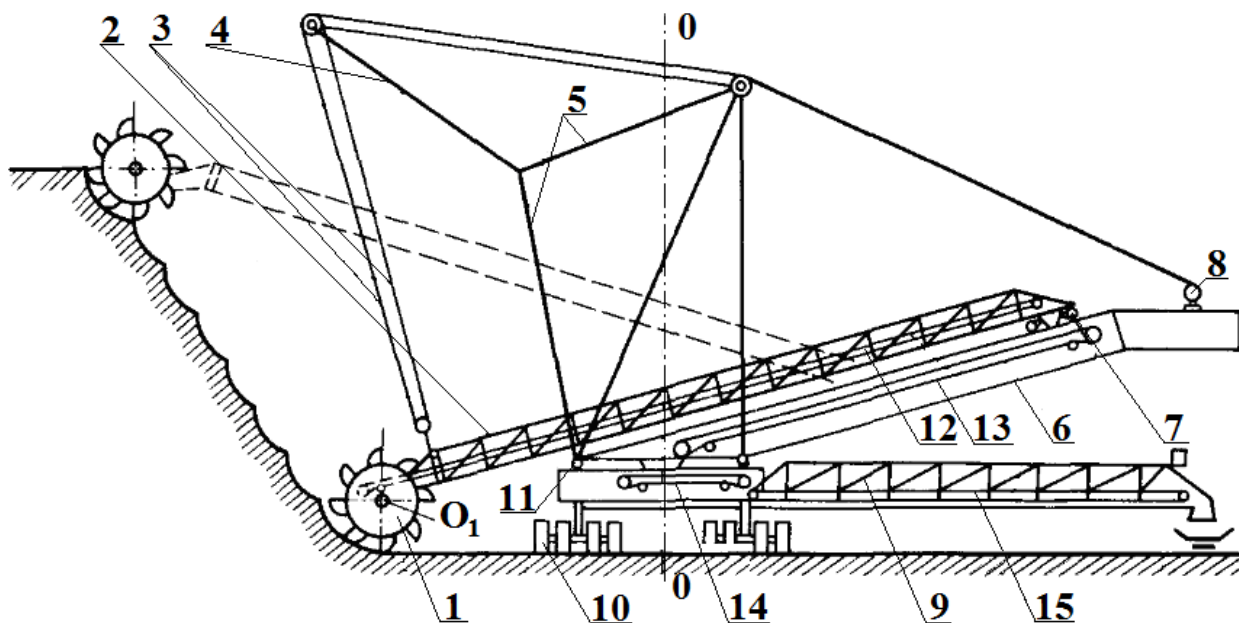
Конструктивна схема роторного екскаватора з висувним візком
